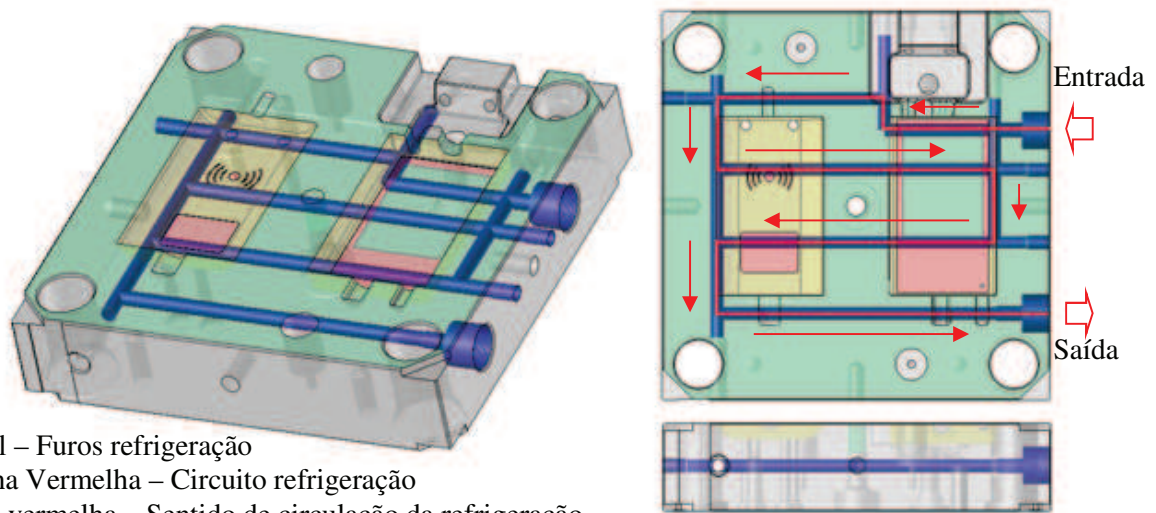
Circuito de refrigeração de uma zona moldante de um molde de injeção.
